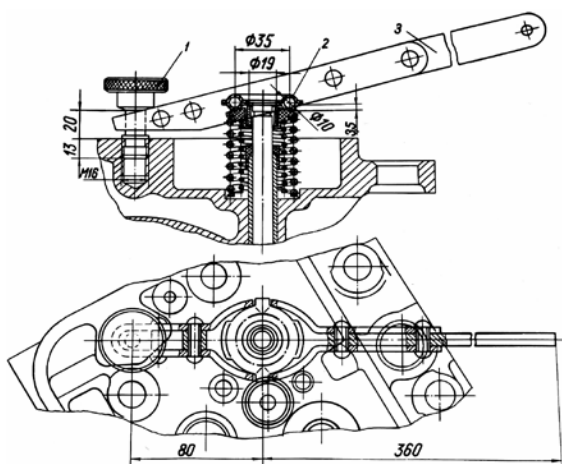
Приспособление для рассухаривания клапанов
